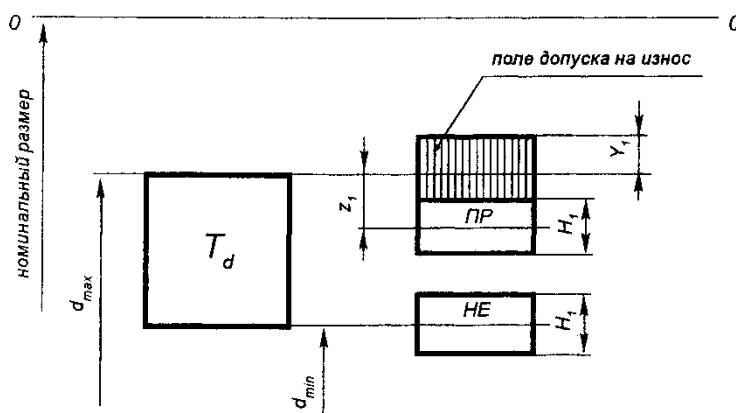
Схема расположения полей допусков калибров для контроля валов изготовленных по квалитетам 6, 7 и 8 при номинальных размерах до 180 мм (для размеров валов изготовленных по квалитетам от 8 до 17, $Y = 0$)
